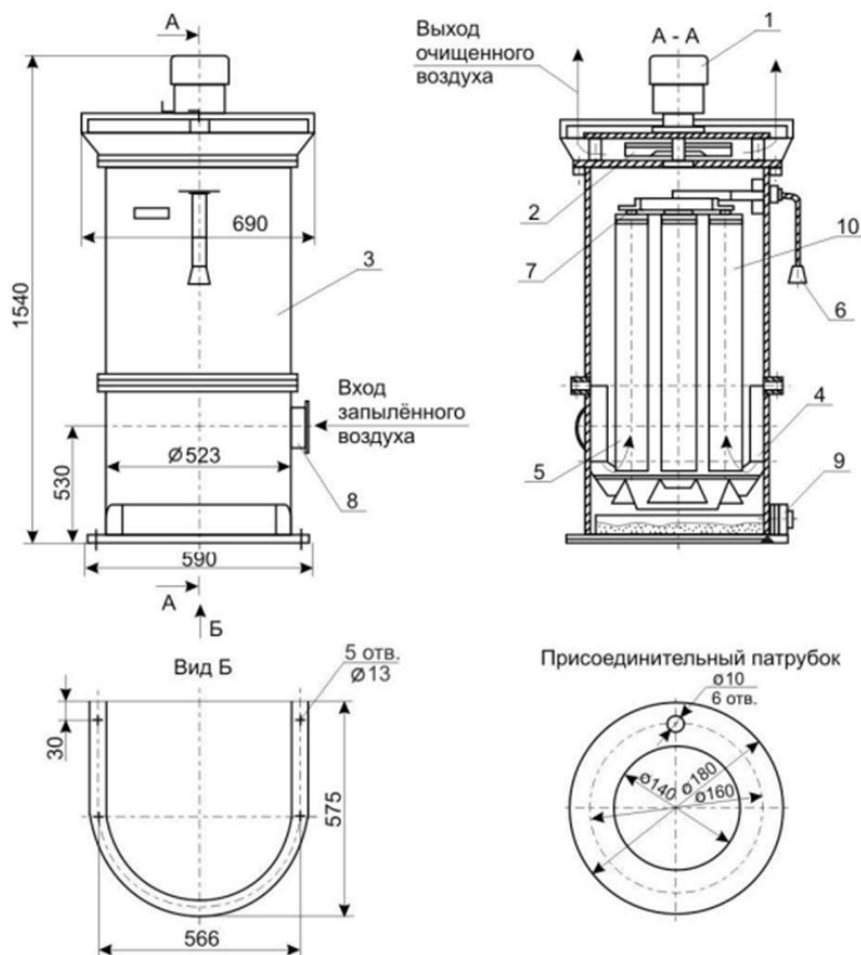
Пылеулавливающий агрегат ЗИЛ-900М:
